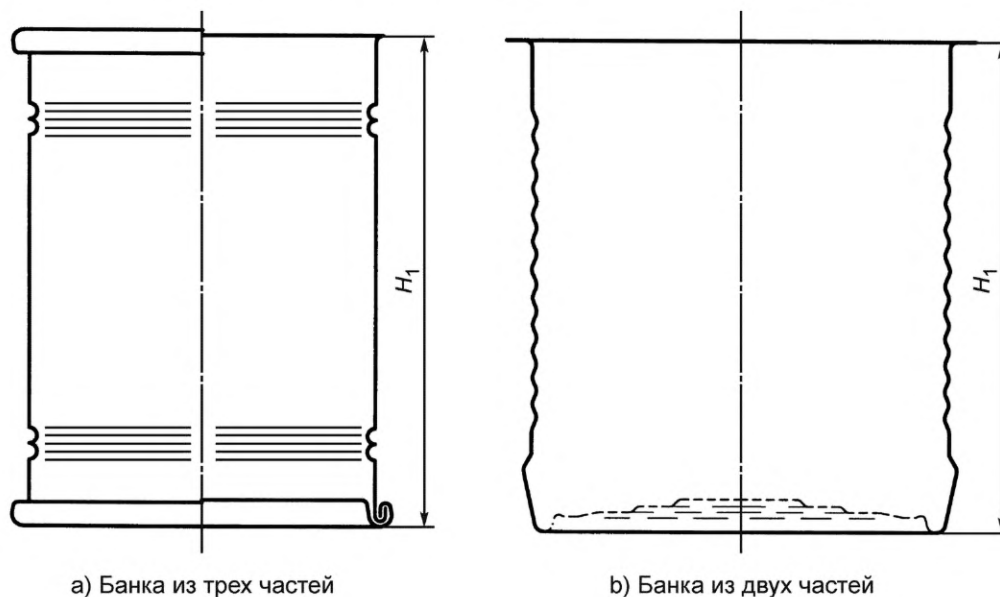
Измерение высоты корпуса банок, открываемых сверху
